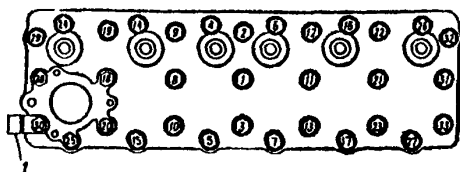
Порядок затяжки гаек головки цилиндров и установка скобы крепления сливного шланга из испарителя автомобилей ГАЗ-52-07 и ГАЗ-52-08
